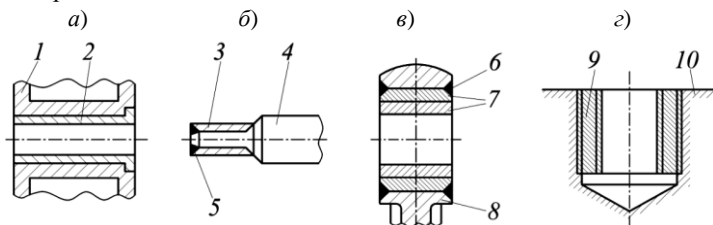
Схемы постановки дополнительной ремонтной детали:
